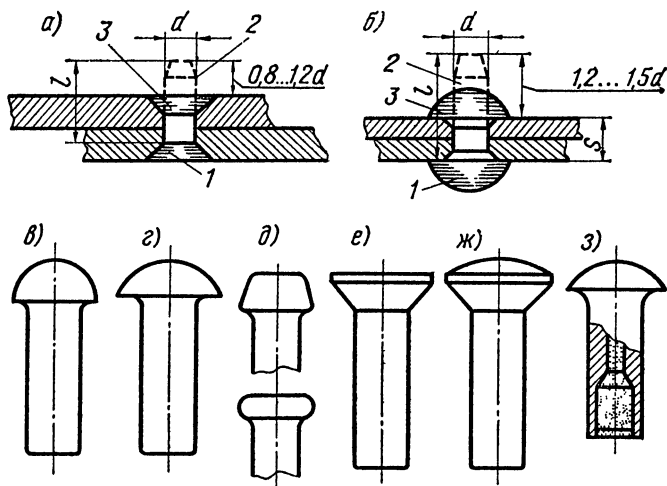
Элементы заклепочного соединения: а — с потайной головкой; б — с полукруглой головкой; в — с полукруглой высокой головкой; г — с полукруглой низкой головкой; д — с плоской головкой; е — с потайной головкой; ж — с полупотайной головкой; з — взрывная заклепка
